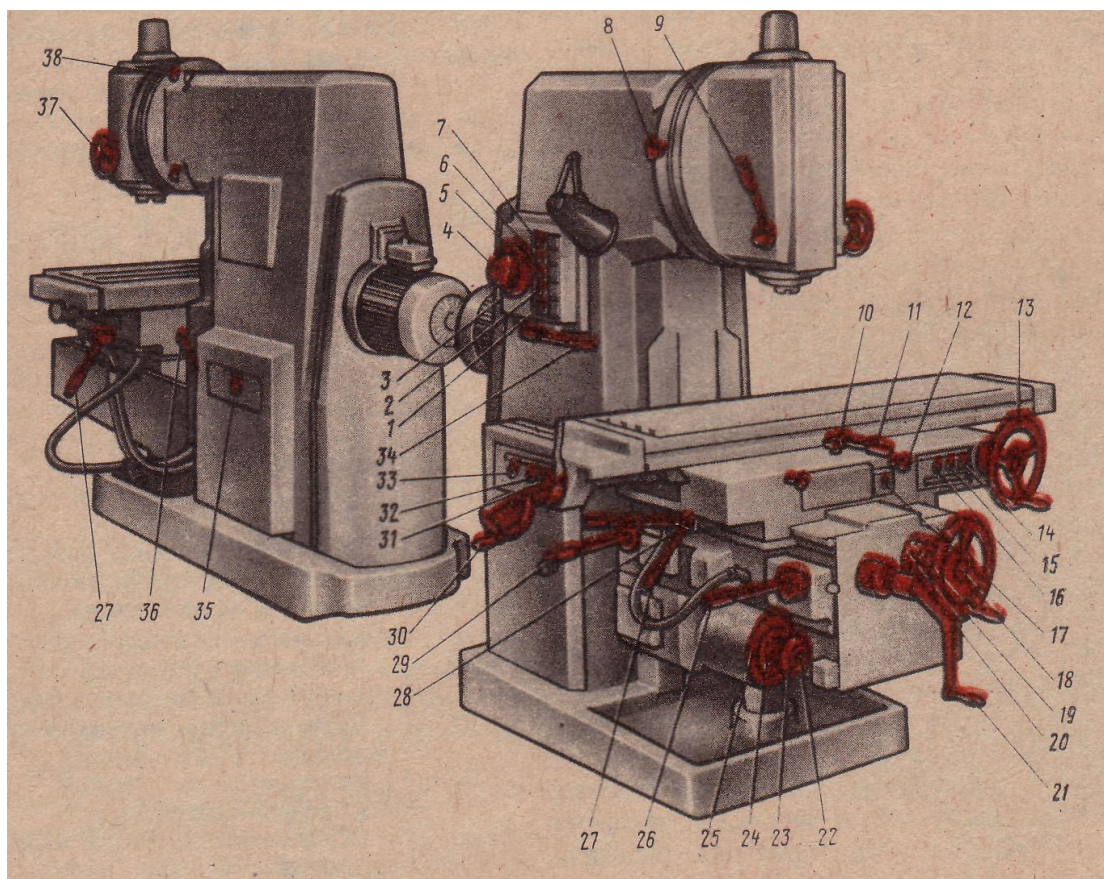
Органы управления консольного вертикально-фрезерного станка
